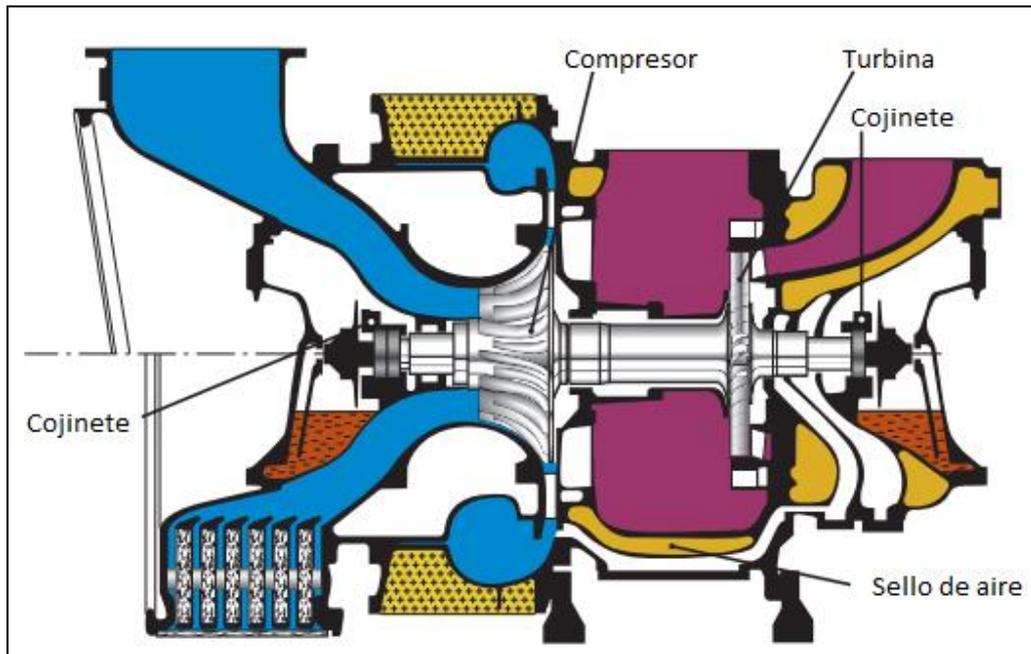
Rotor del Turbocargador VTR sobre los rodamientos.
